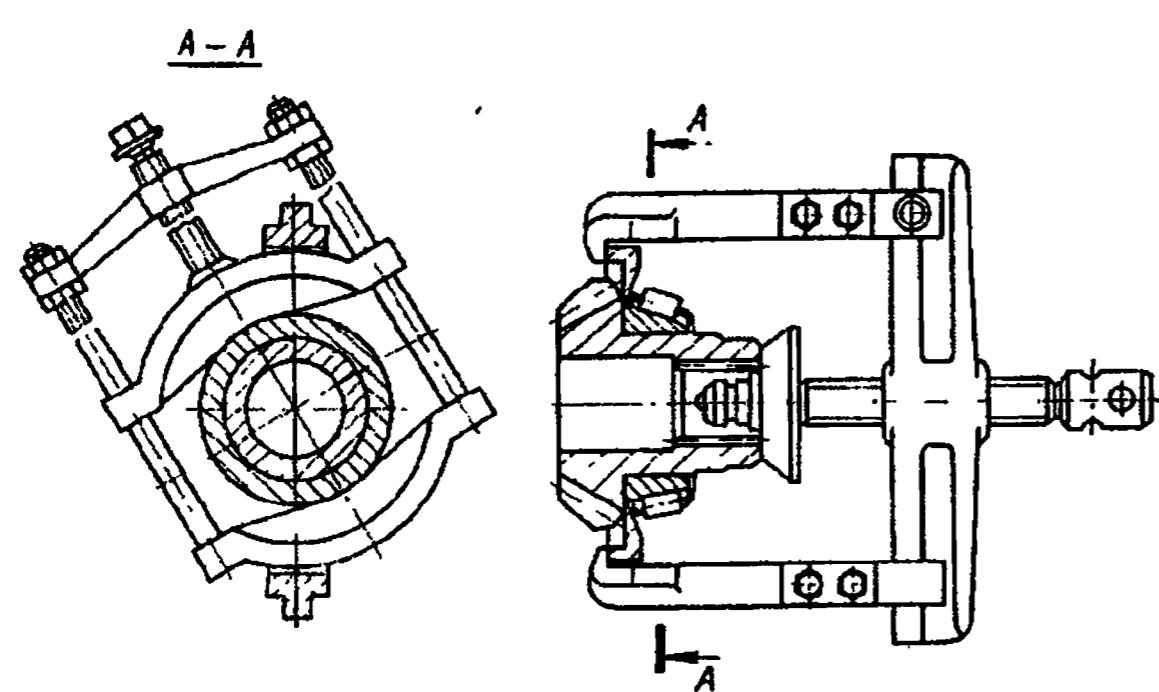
Снятие внутренних колец подшипников ведущих зубчатых колес съемником
